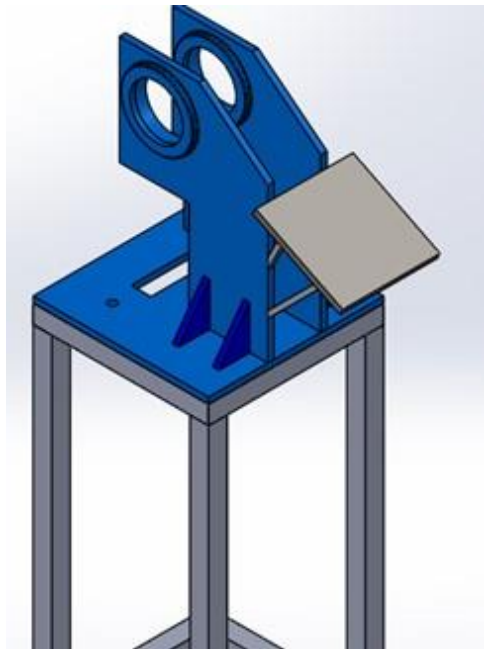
Vista detallada de los elementos de soporte para el motor eléctrico.
